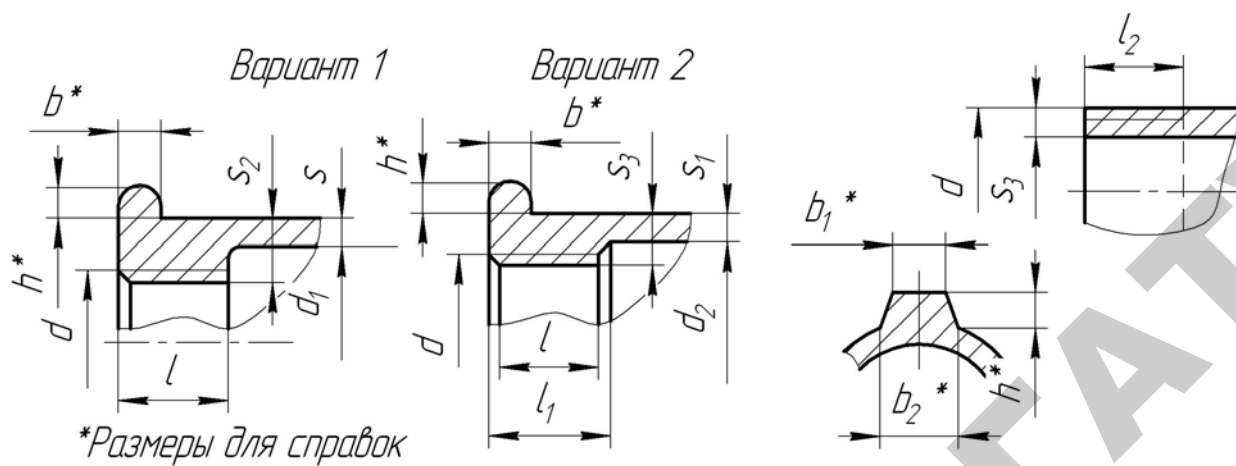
Форма и конструктивные размеры соединительных частей
